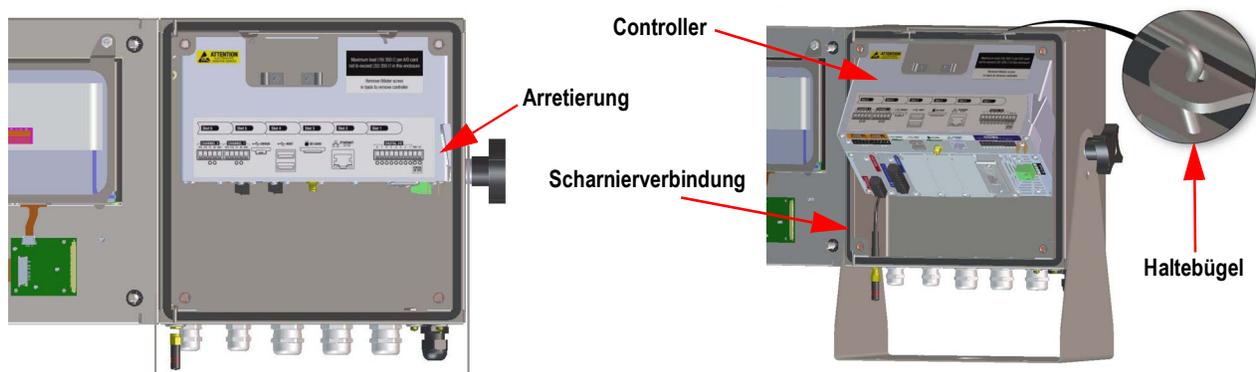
Entfernen der CPU - Universalhalterung
